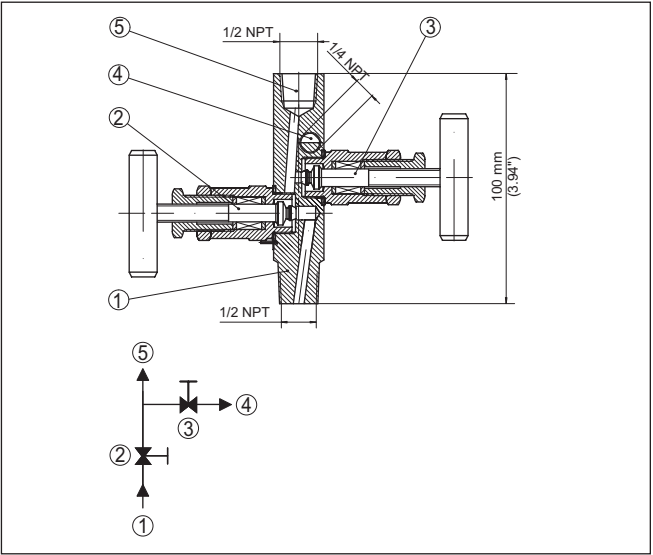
Конструкция двойного запорного вентиля 1/2NPT
